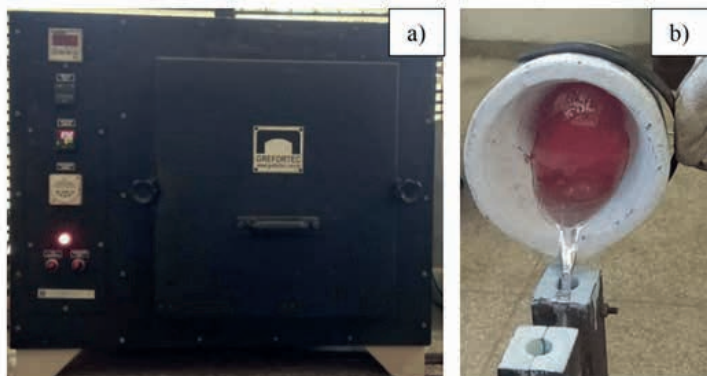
a) Forno utilizado para a fundição; b) Vazamento do metal líquido no molde.
